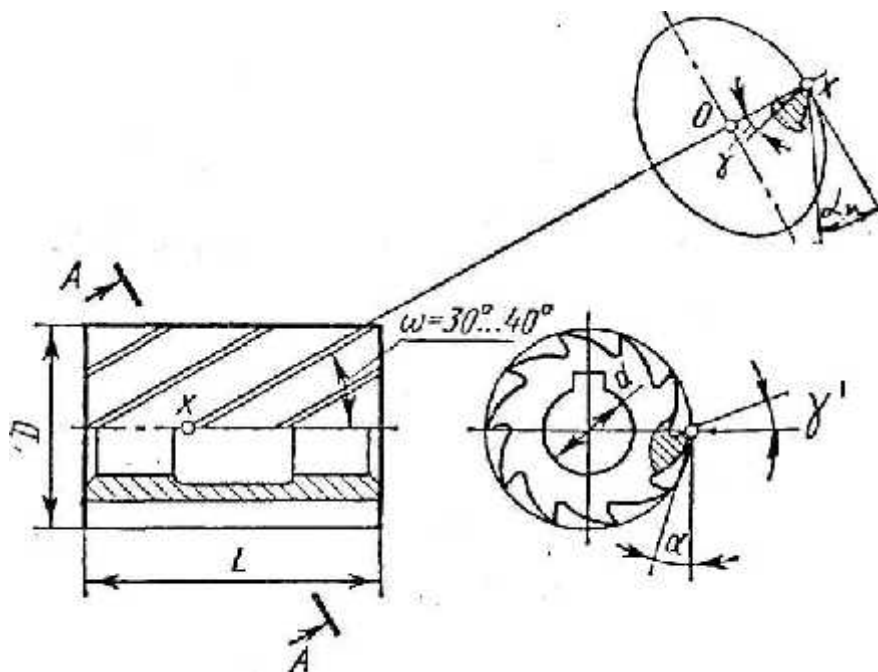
Геометрические элементы режущей части цилиндрической фрезы
